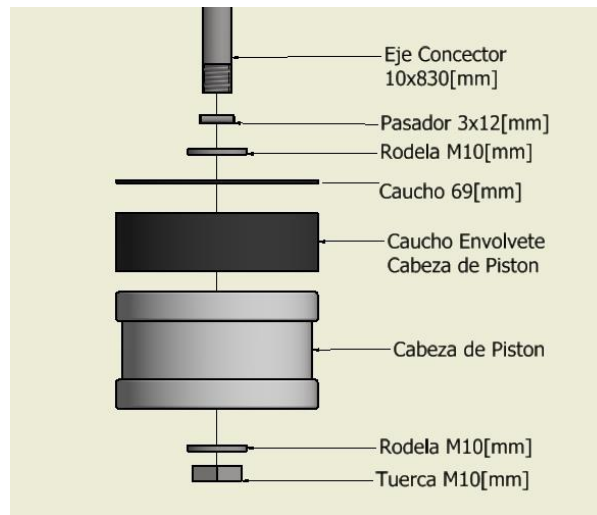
DIMENSIONES DE LA CABEZA DEL PISTÓN Y LOS COMPONENTES DE
